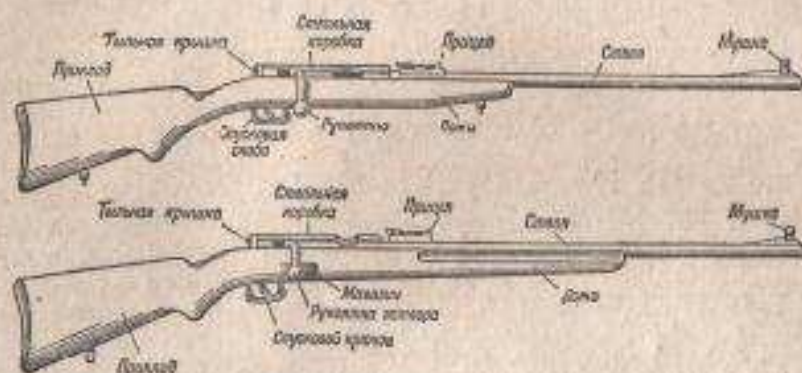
Общий вид малокалиберной винтовки: сверху ТОЗ-8, снизу — ТОЗ-9
